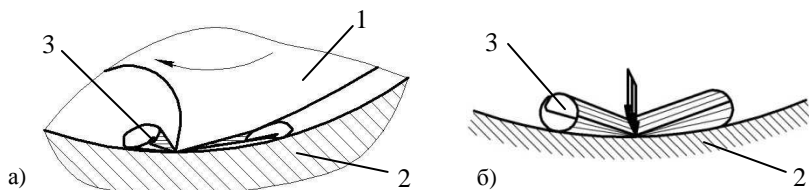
Схематизация процесса деформирования (а) и расчётная схема для определения внутренних силовых факторов при повторном взаимодействии отделенной стружки с фрезой (б): 1 – фреза; 2 – обрабатываемый паз; 3 – стружка
